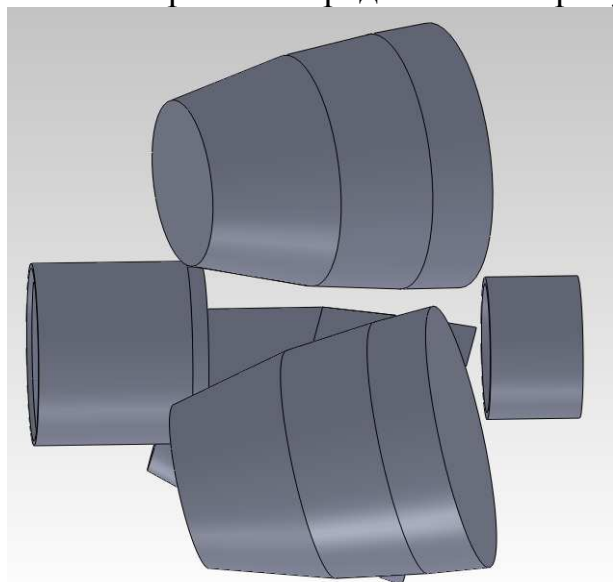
Сборка поперечно-винтовой прокатки в среде SolidWorks
